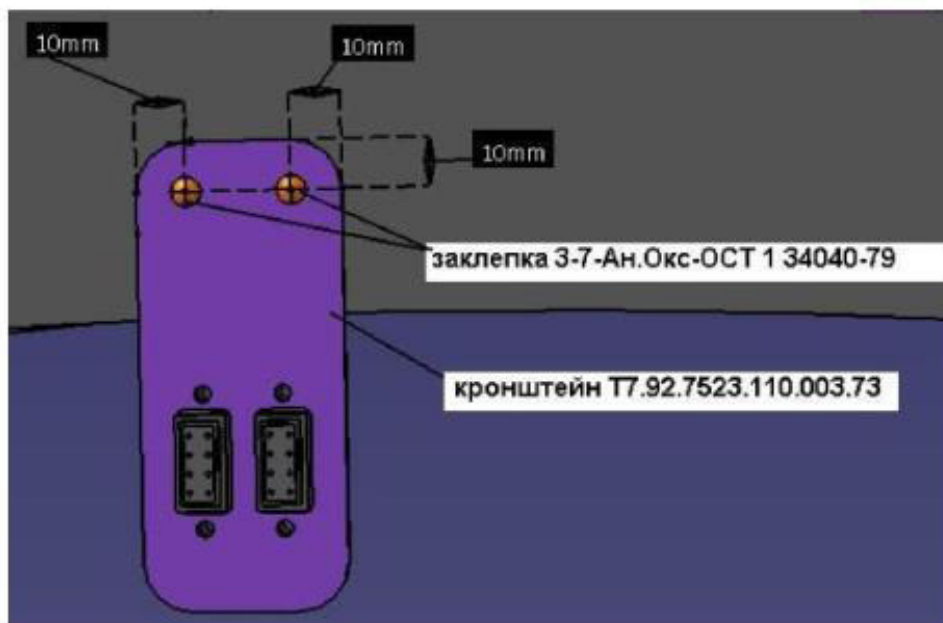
установка заклепок на кронштейн Т7.92.7523.110.003.73
